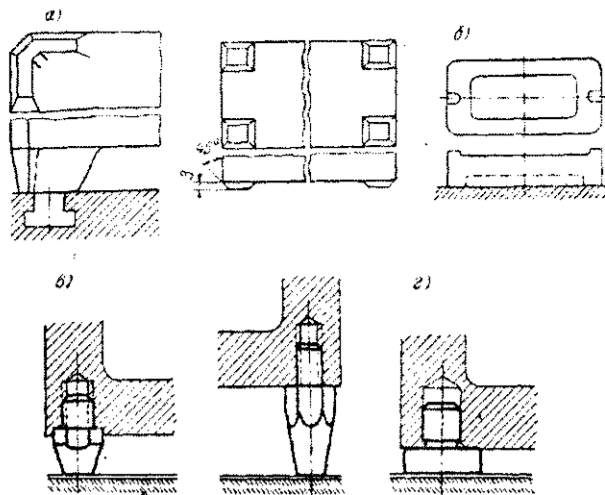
Опорные элементы корпусов: а, б – ножки и пластики, выполненные за одно целое с корпусом; в и г – стальные приставные ножки (МН 368-60)
